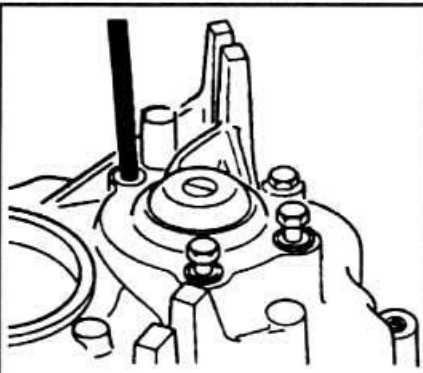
Приспособление BMW 23 2440, вставленное через резьбовое отверстие задней крышки для фиксации пластины
